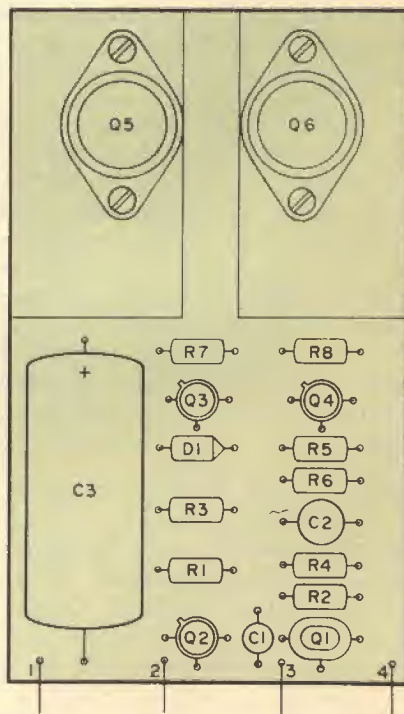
Sistemate e saldate tutti i componenti sul circuito stampato, con questa disposizione.
